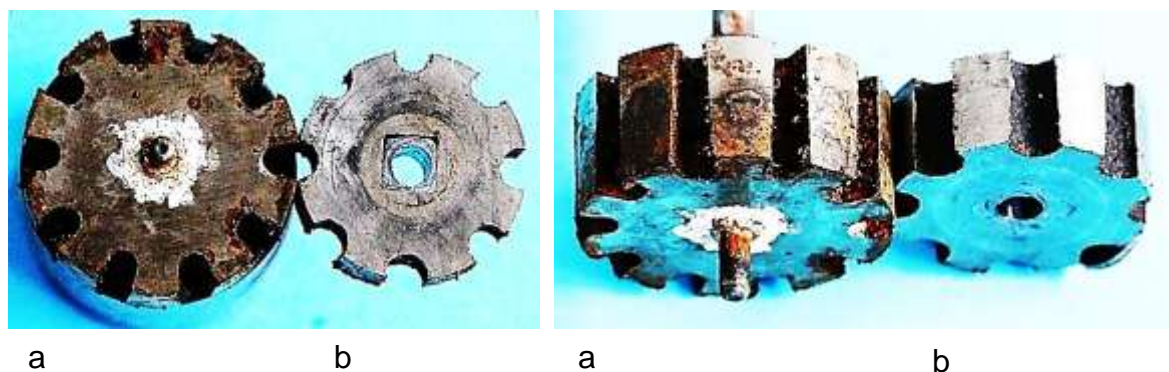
Abmessungen des 10- und des 8-poligen Polrades: a) Polraddurchmesser 36 mm, axiale Länge 15 mm, b) Polraddurchmesser 32 mm, axiale Länge 12 mm
